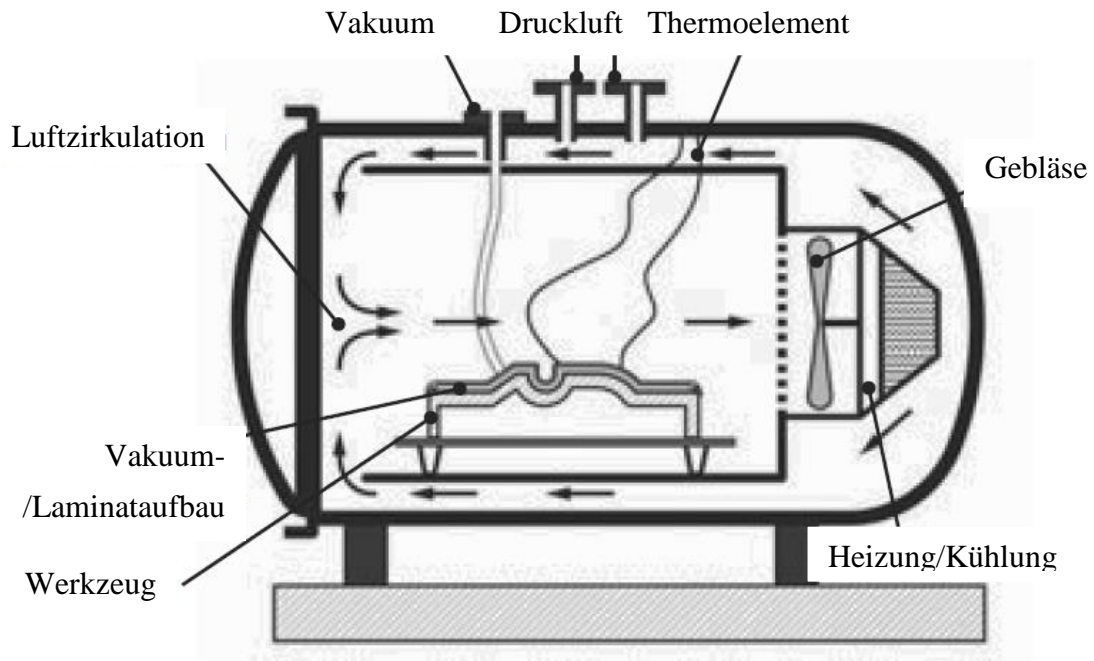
Grundaufbau eines Autoklaven für die Bauteilherstellung nach dem Autoklavverfahren [34]
